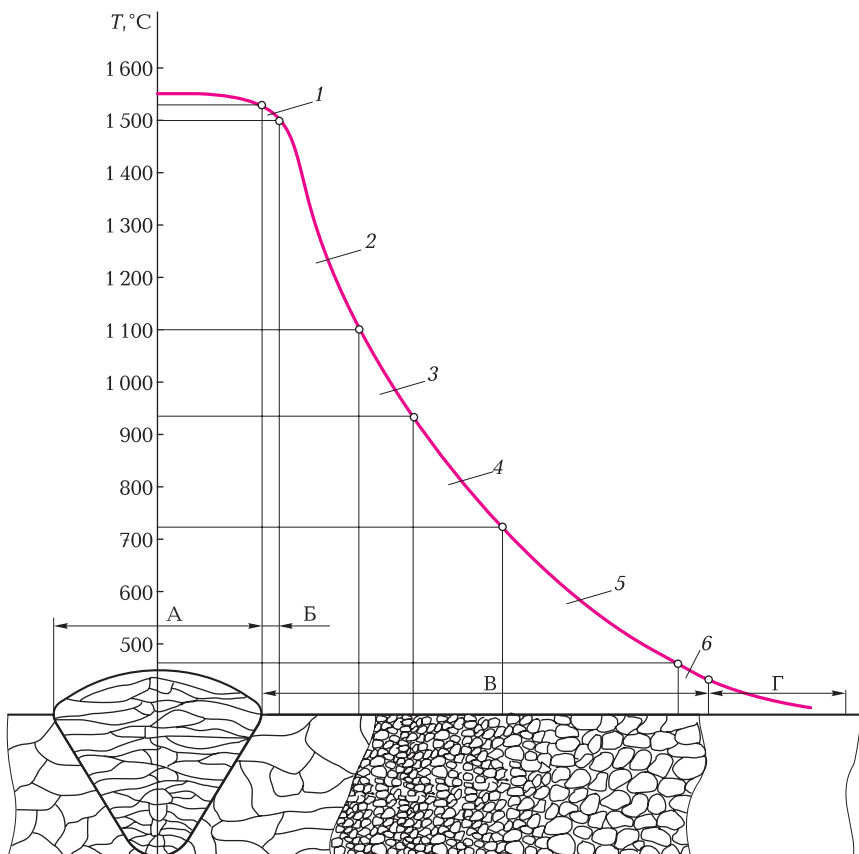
Термический цикл сварки (зоны А...Г сварного соединения и участки 1...6 околошовной зоны):
